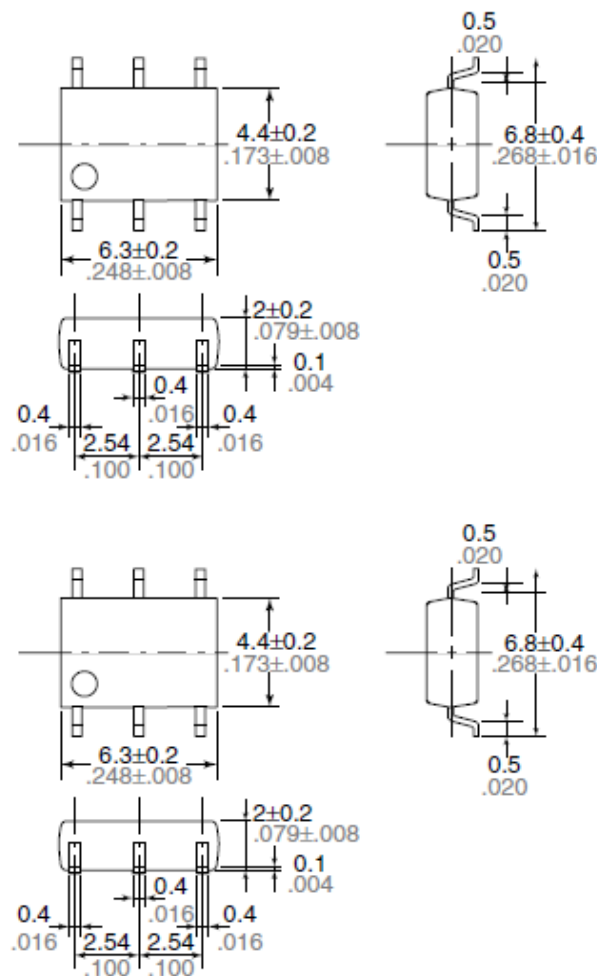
Габаритні розміри уніфікованого корпусу типу SOP-6
